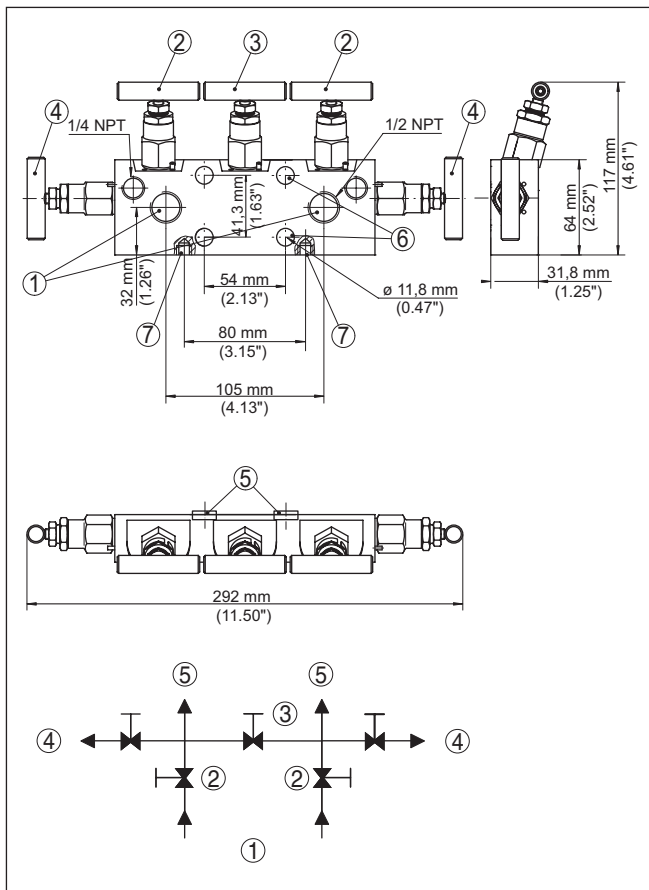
Construção bloco de 5 válvulas conforme EN 61518
